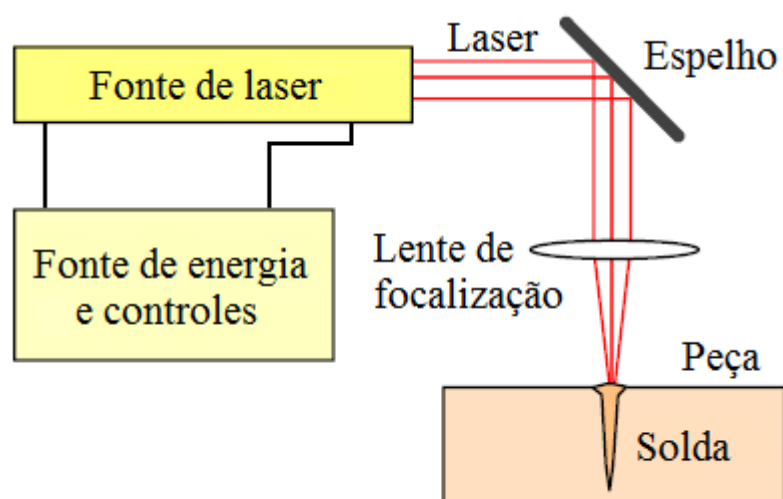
Elementos de um sistema típico para soldagem a laser <sup>70</sup>
